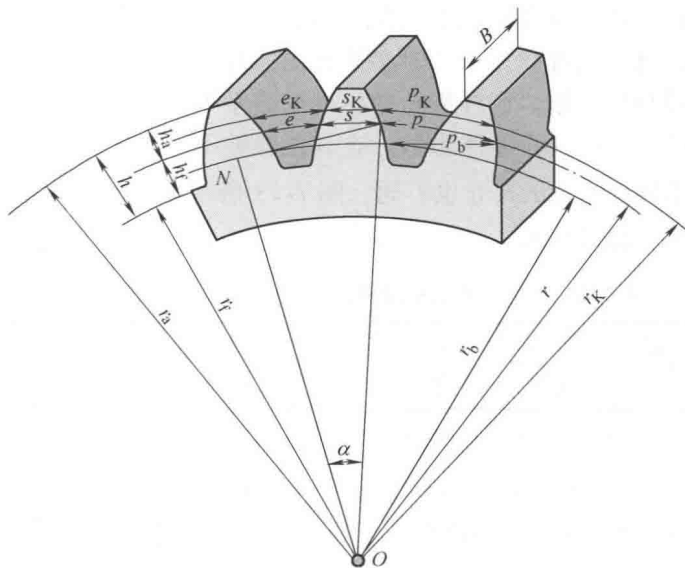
渐开线直齿圆柱外齿轮各部分名称
